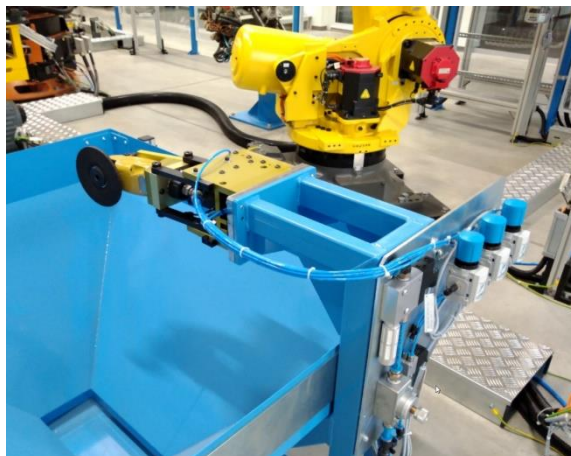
Pneumatické radiální vřeteno pro frézování - odjehlování
